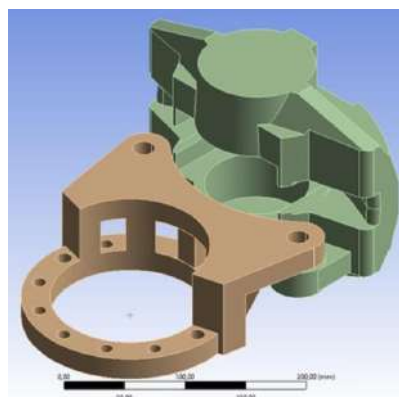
3D - Модель сварного кронштейна
